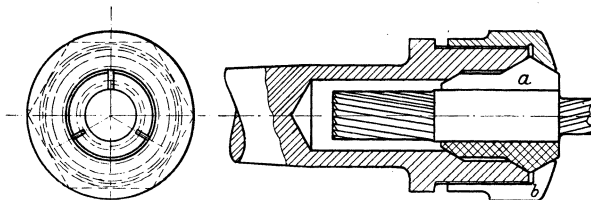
Das Klemmfutter für zylindrische Fräferschäfte.
